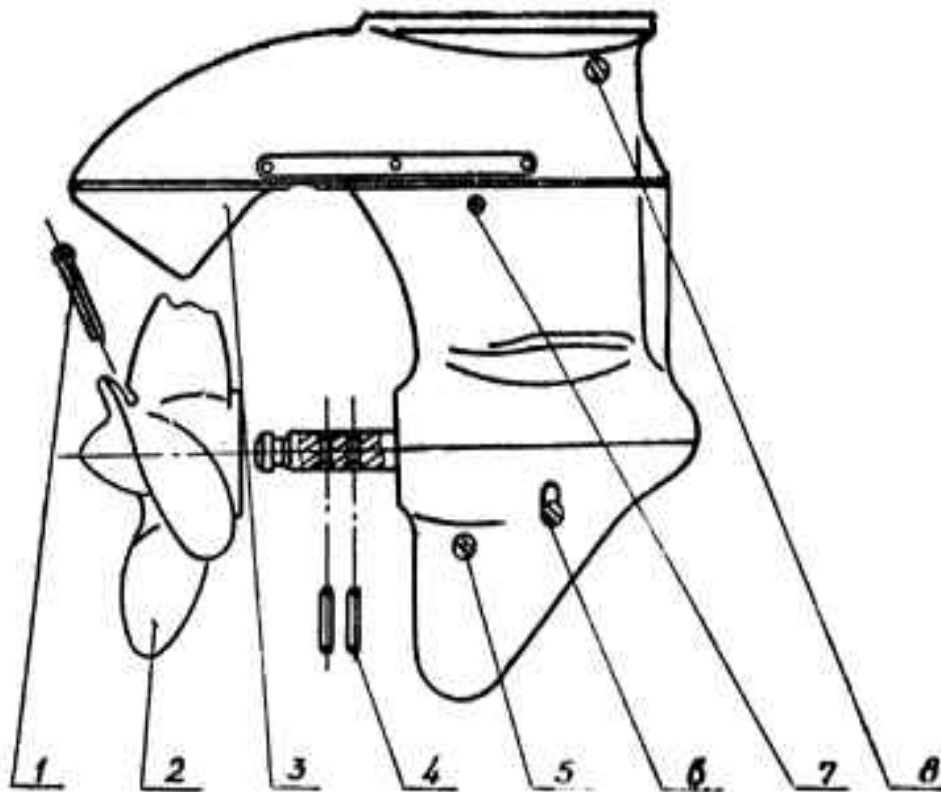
Расположение пробок для залива и слива смазки редуктора
